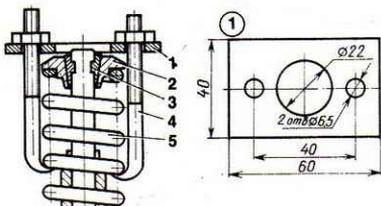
Разборка клапанного узла: 1 — пластина; 2 — тарелка; 3 — сухарик; 4 — крюк; 5 — пружина.
